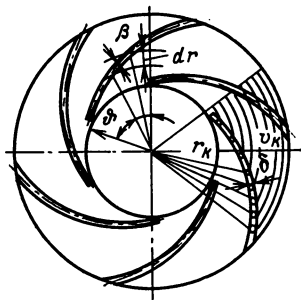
Построение цилиндрической лопатки центробежного колеса
